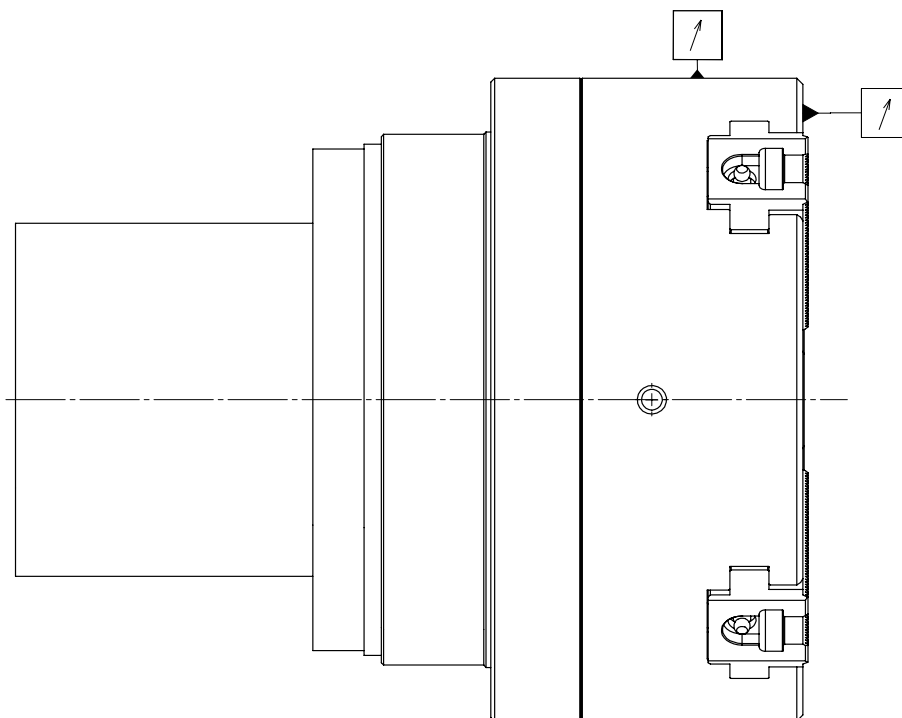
Mandrino di serraggio montato sulla flangia intermedia
